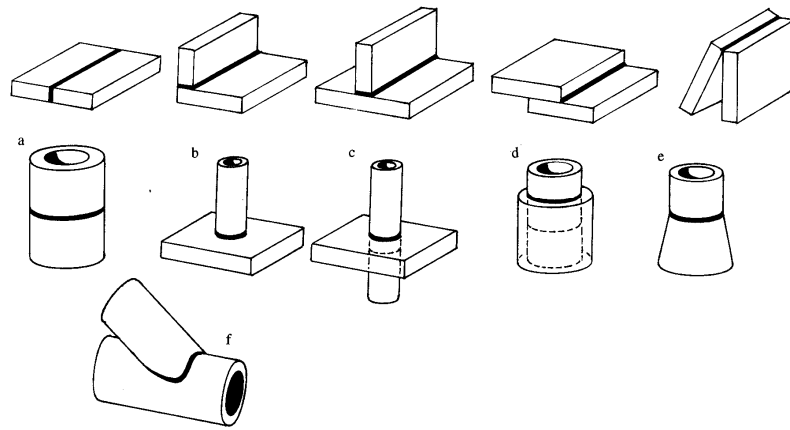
Tipos básicos de soldadura en planchas y tubos.
